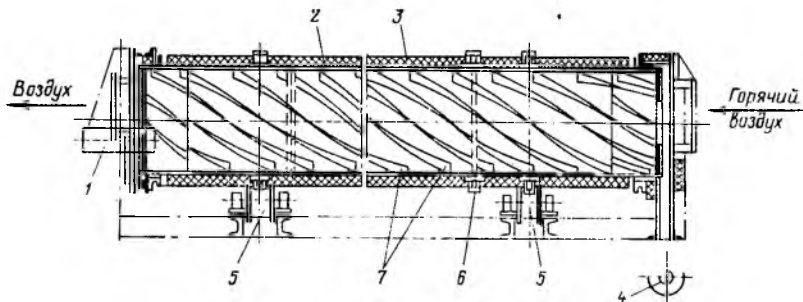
Общий вид барабанной сушилки гидрокарбоната натрия:
